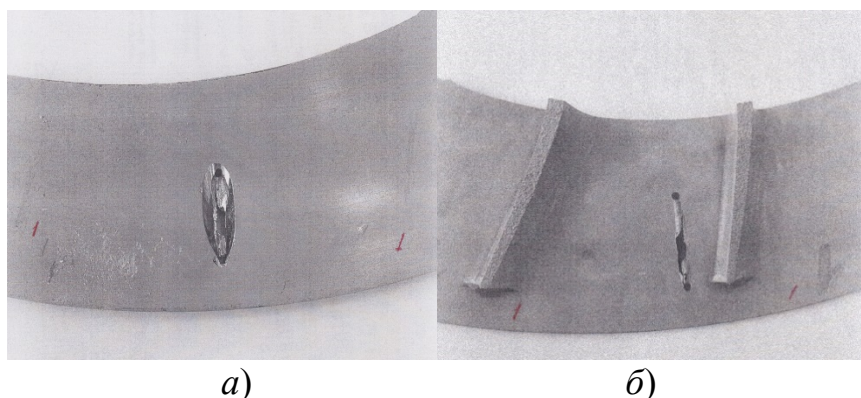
Разделка ранее наплавленного образца: а) вид с наружной стороны; б) вид с обратной стороны покрывающего диска
